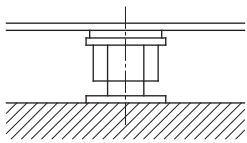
Нівелірні гвинти на поверхні фундаменту
